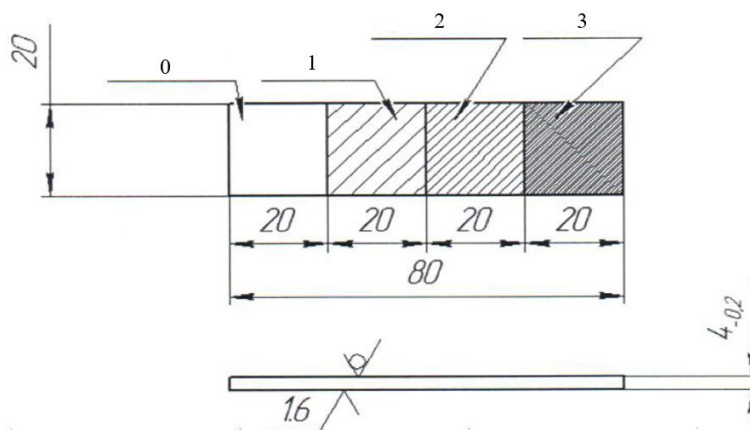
Схематичное расположение обрабатываемых поверхностей заготовок
